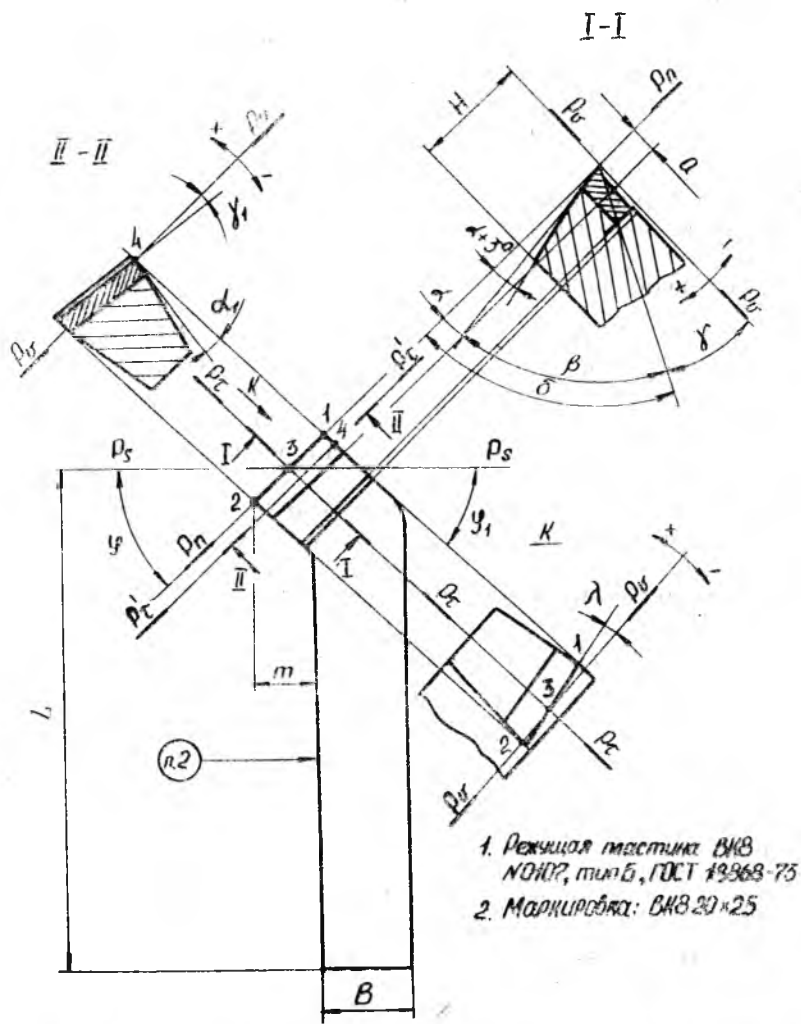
Эскиз токарного проходного резца с отогнутой головкой
